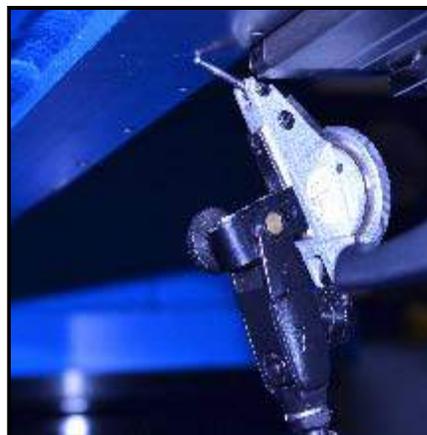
CONTACTO ENTRE EL INDICADOR Y LA SUPERFICIE DE ATAQUE DE LA MÁQUINA
